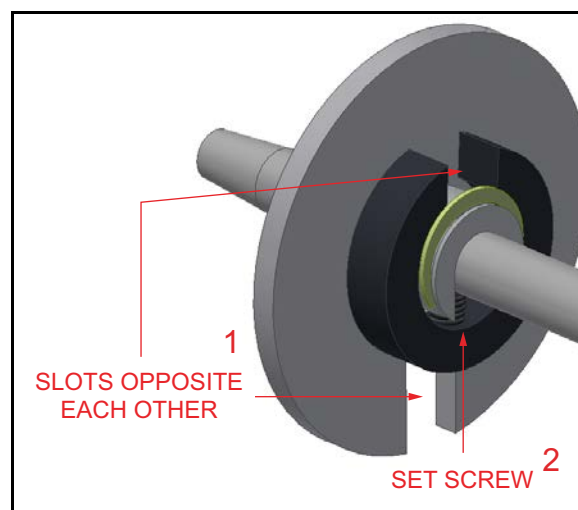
ПОВЕРНУТАЯ ВТУЛКА С РАСПОЛОЖЕННЫМИ ДРУГ НАПРОТИВ ДРУГА ПАЗАМИ
